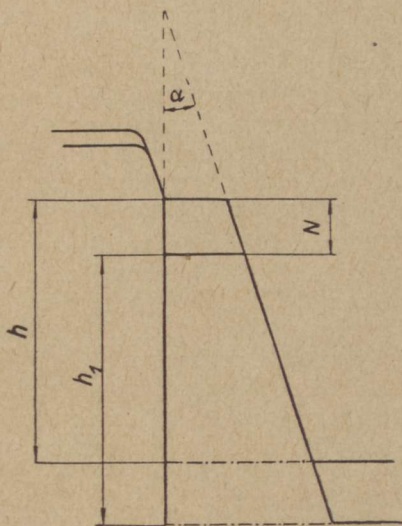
Bemessung der Flanschhöhen nach E. Kirchberg.
